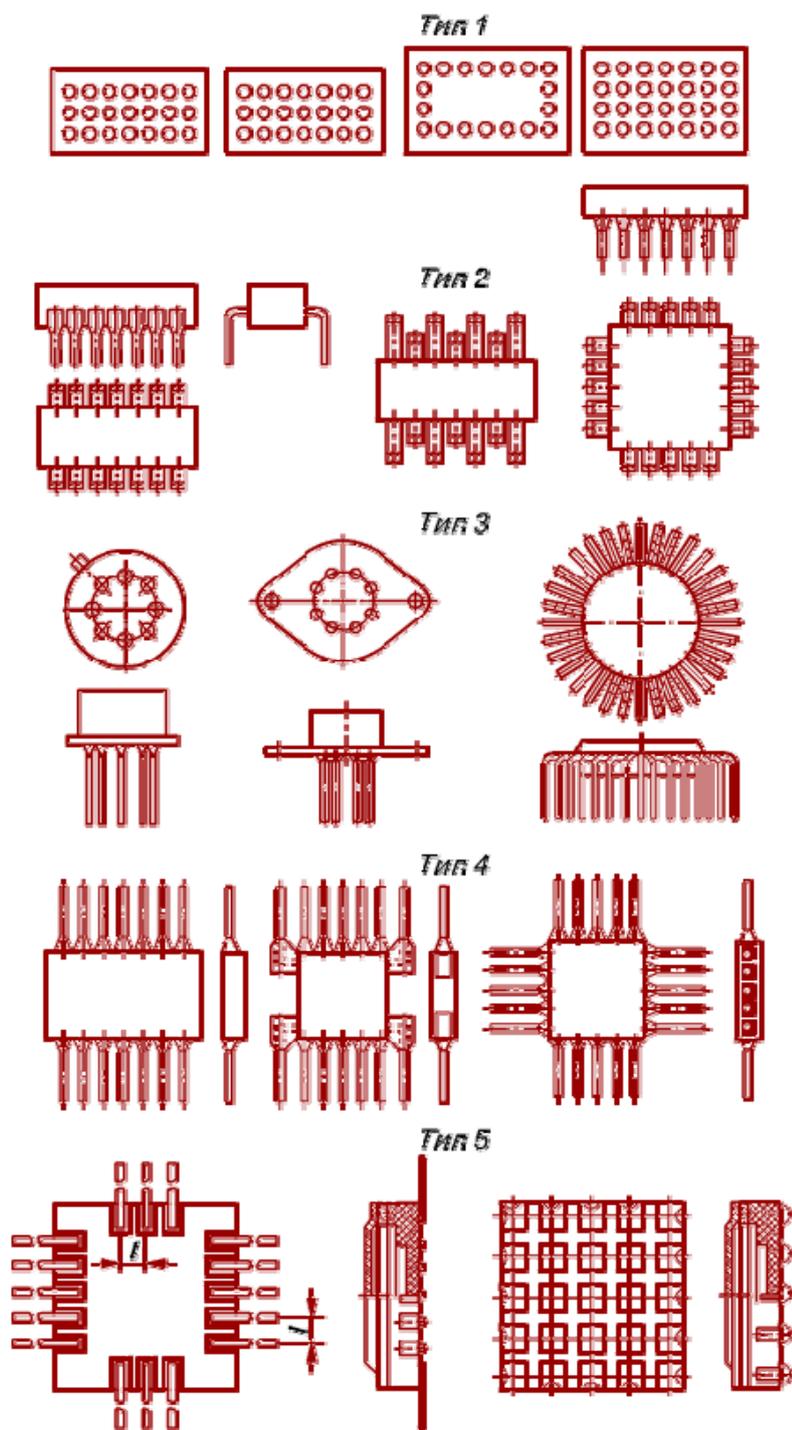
Типы корпусов ИС (1 – шаг расположения выводов)
